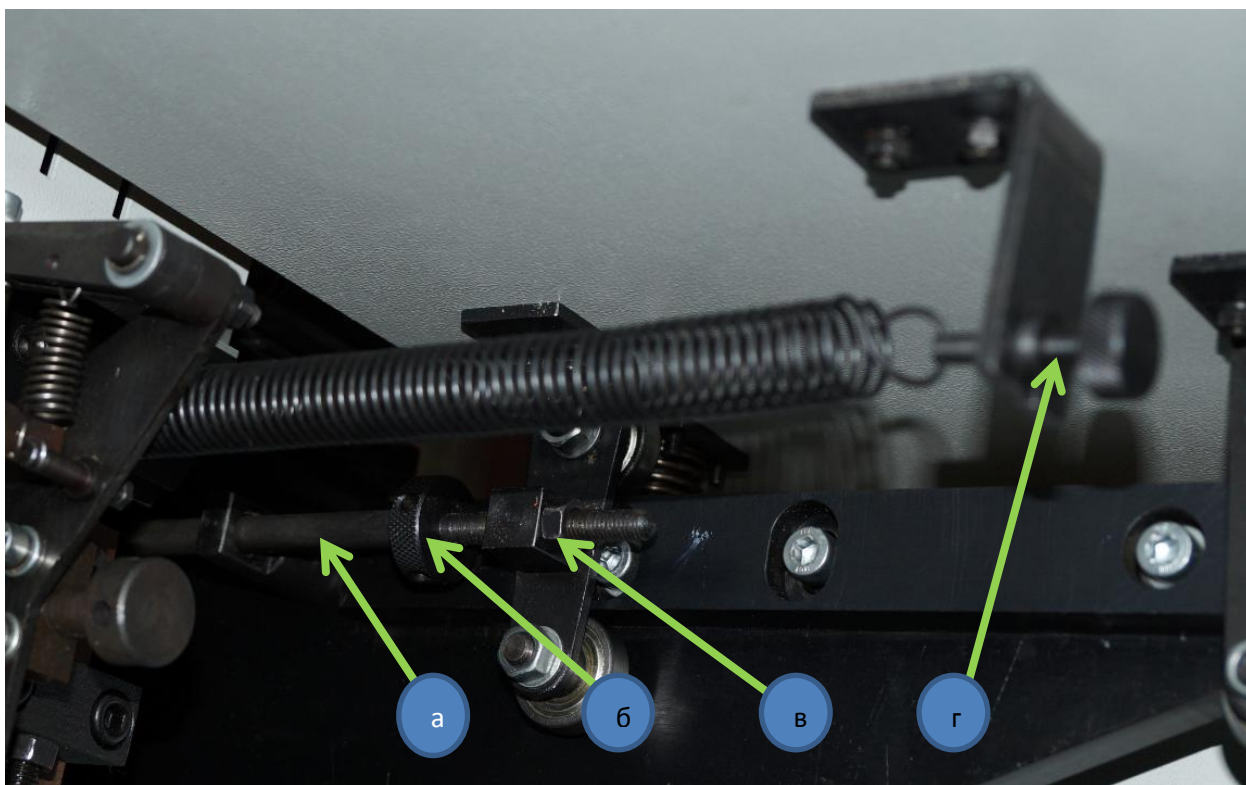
Вид рабочего стола снизу. А-подвижный толкатель; б- регулируемый упор стола; в- контргайка упора стола; г- фиксатор пружины
